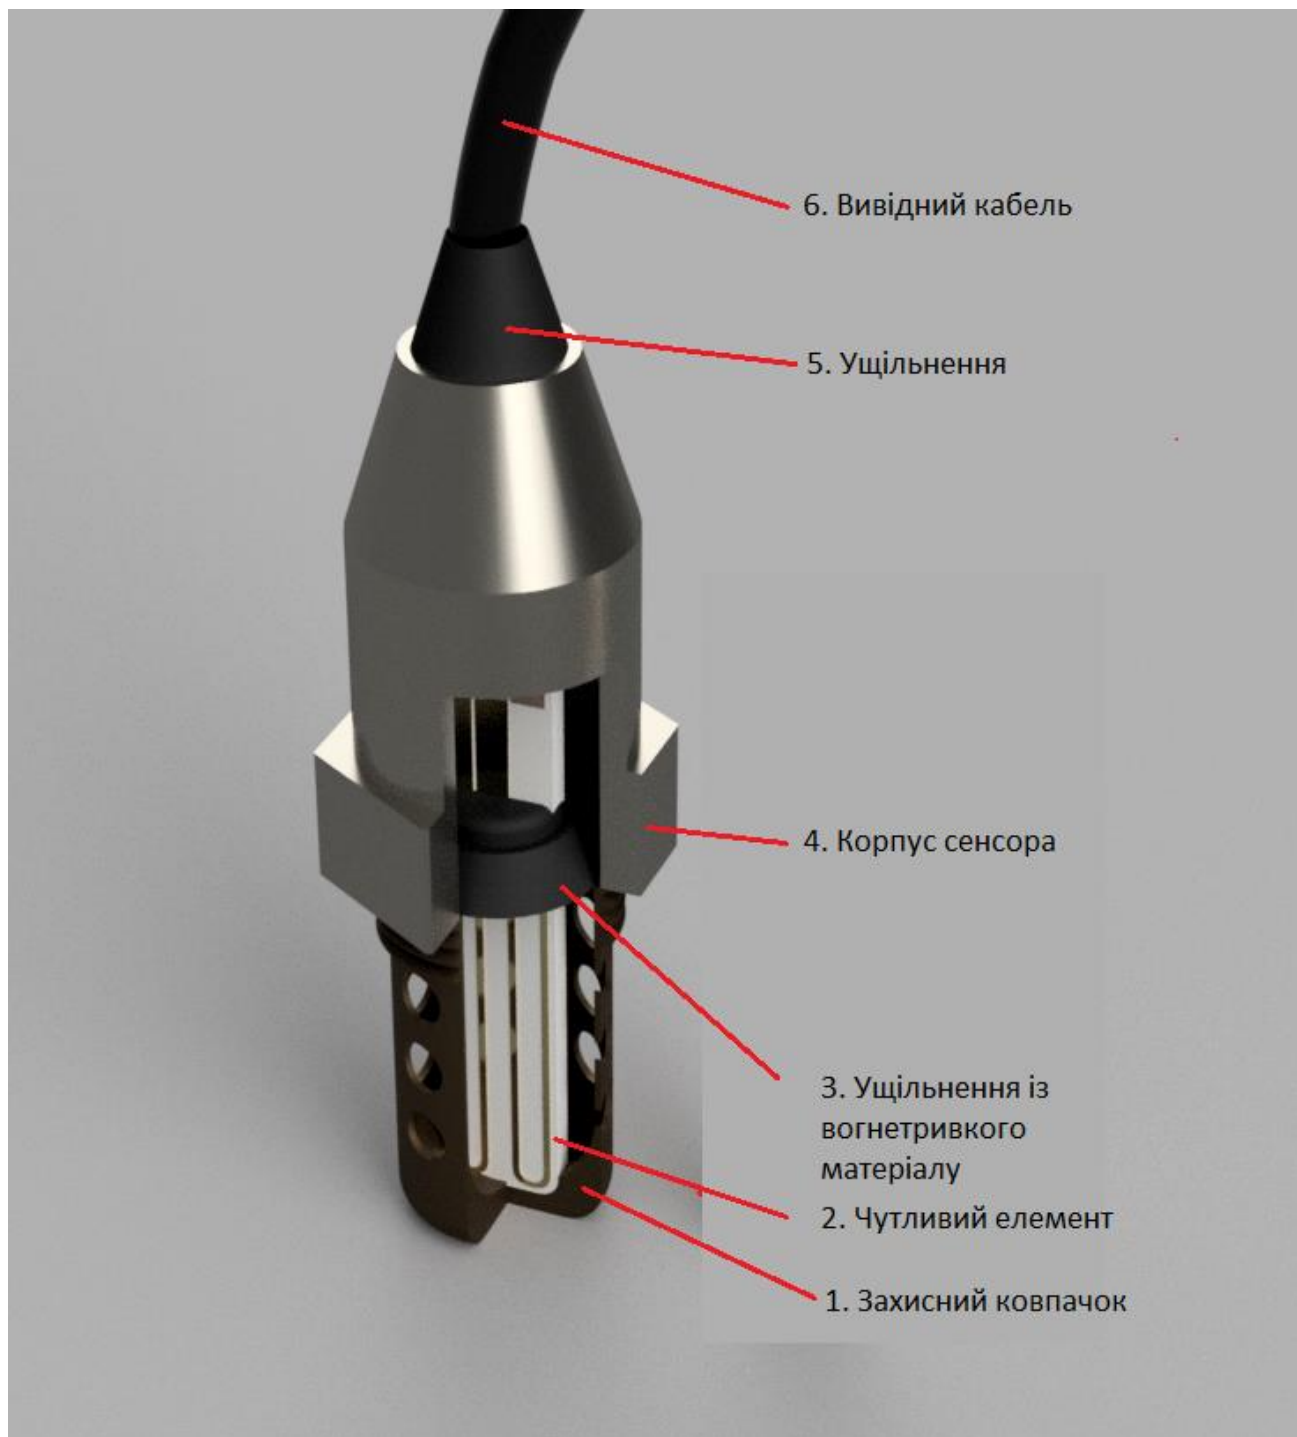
3D розріз зібраного сенсора, на якому показані всі конструктивні деталі а також їх внутрішнє розташування.
